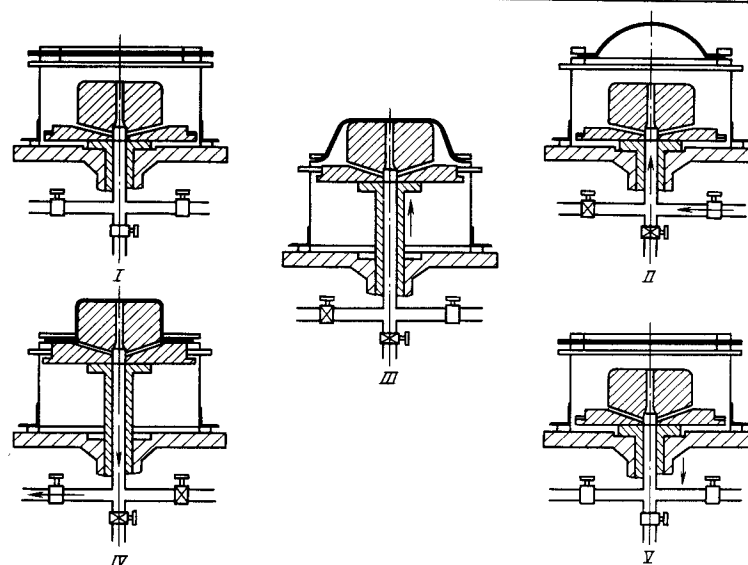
Схема позитивной формовки с предварительной пневматической вытяжкой
